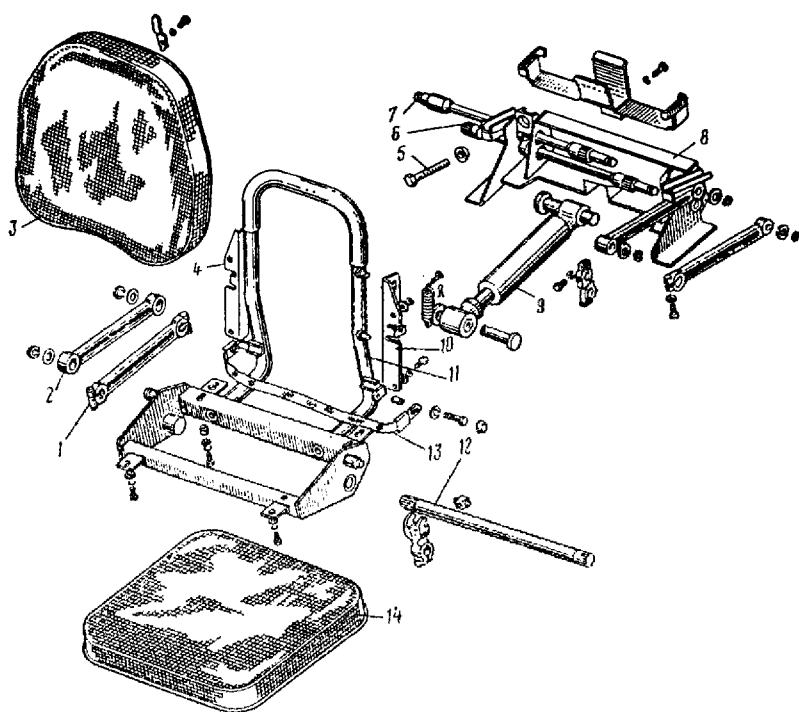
Детали сиденья оператора тракторов семейства ЮМЗ (кроме 8070...8280): 1 - нижний рычаг; 2 - верхний рычаг; 3 - подушка спинки; 4 - правый сектор; 5 - регулировочный блок; 6 - нижний торсион; 7 - верхний торсион; 8 - кронштейн; 9 - амортизатор; 10 - левый сектор; 11 - остов сиденья; 12 - стабилизатор; 13 - ремень безопасности
